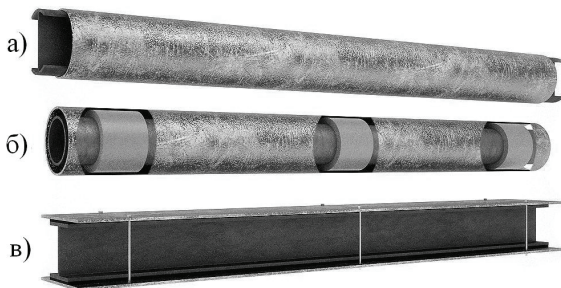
Схема конструкций гасителей в виде жесткой вставки: а – при помощи внутренней конструкции; б – с промежуточной прокладкой между гасителем и шиной; в – внешние накладки.
